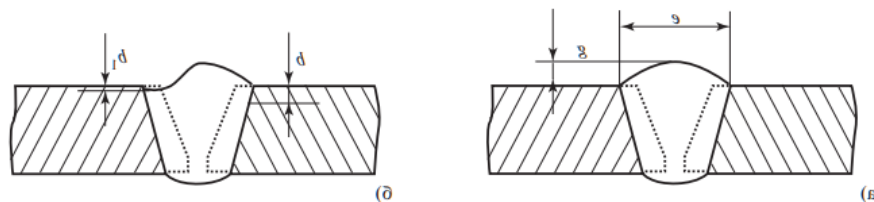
Размеры кольцевого шва сварного соединения, подлежащие измерительному контролю: а) размеры шва сварного соединения: е – ширина; g – высота; б) дефекты шва сварного соединения: b – глубина несплавления, выходящего на поверхность; b1 – глубина подреза
